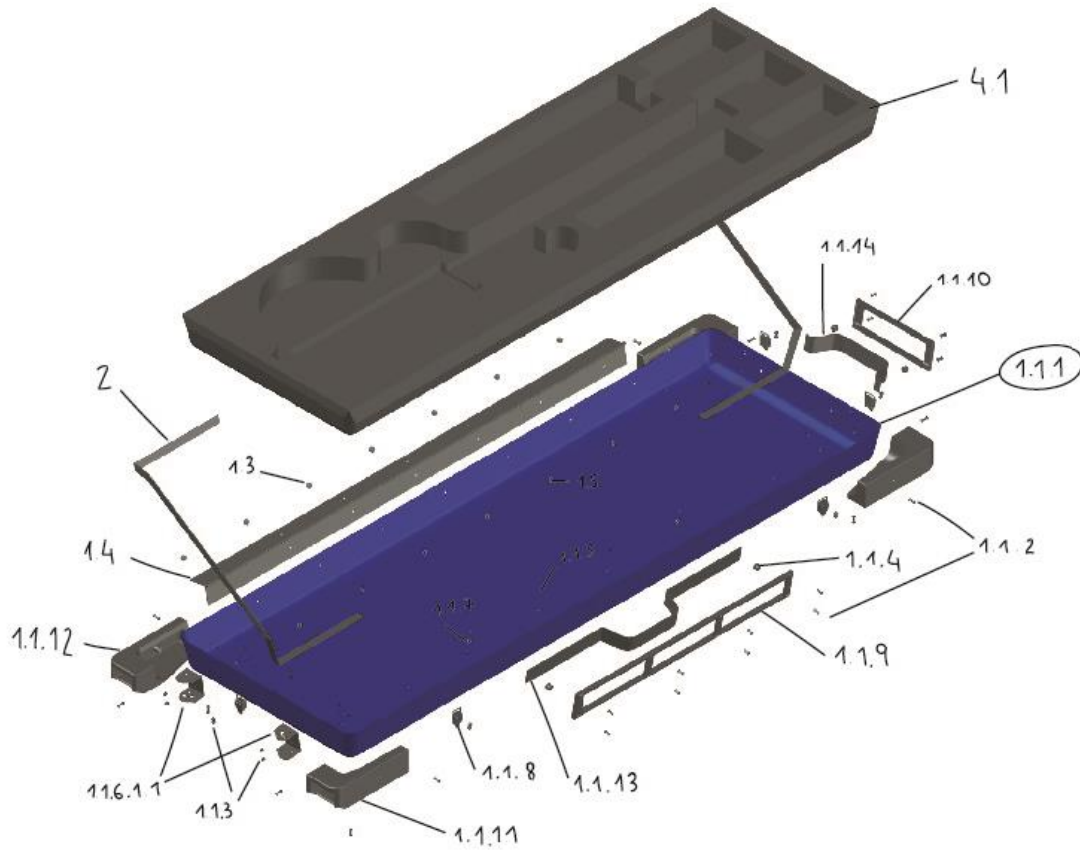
Explosionado de relaciones pieza 1.1.1
